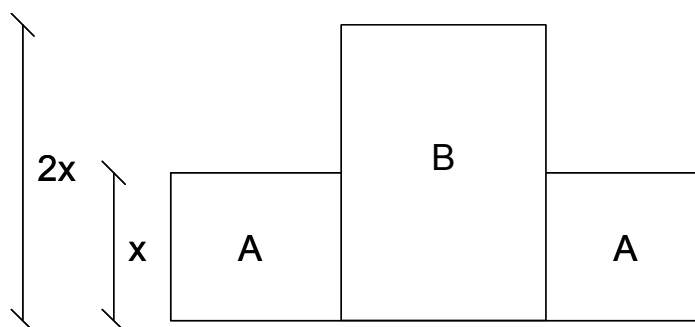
Desenho esquemático do perfil antes da laminação.
